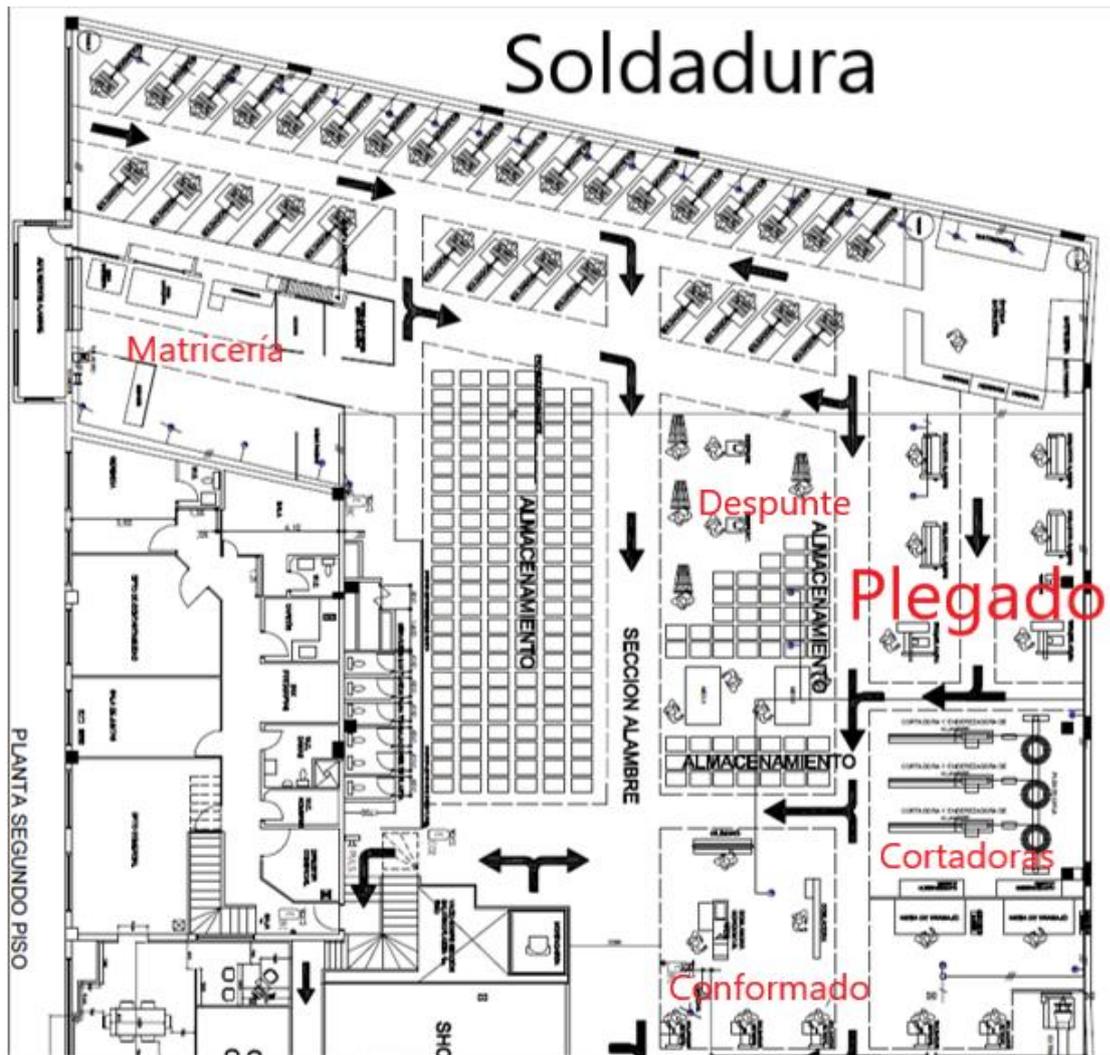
Plano actual de la sección de Alambre. Modificado de Planos Algamar S.A
